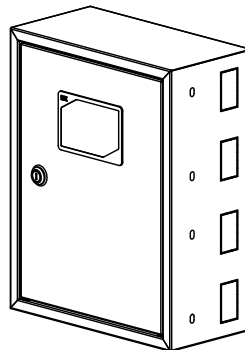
Общий вид корпуса ЯУР-380-300
